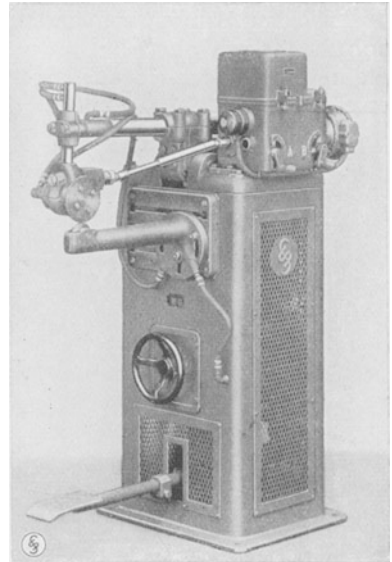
Nahtschweißmaschine mit Stromunterbrechung.
